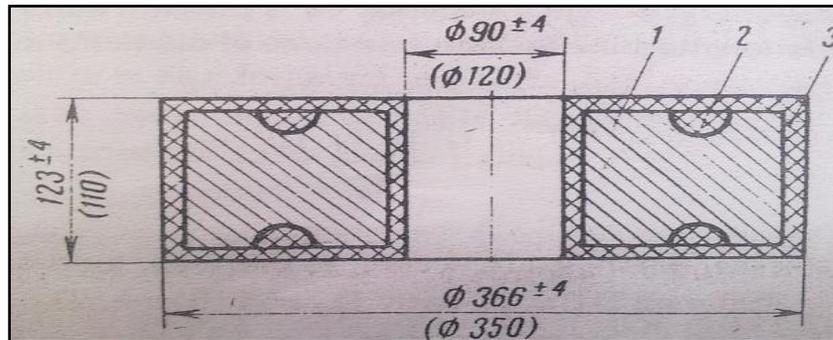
Dibujo del forjado de un disco de engranaje: 1) contorno de un engranaje después del maquinado; 2) sobreespesor de la forjadura; 3) contorno de la forjadura del disco de engranaje.
